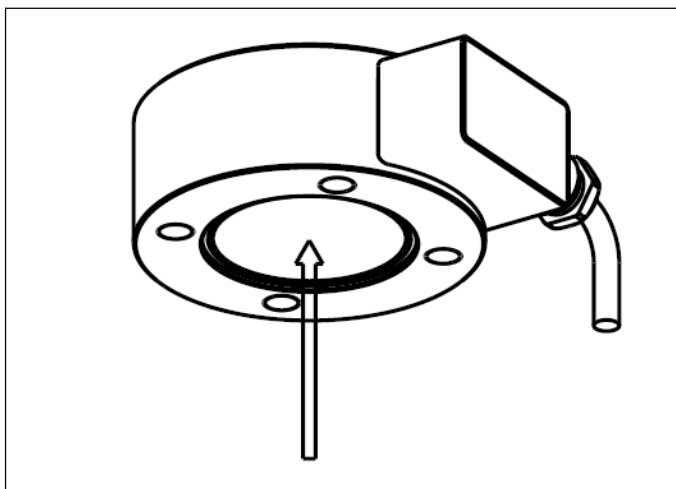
La lamina di protezione sul fondello del sensore non deve essere danneggiata, altrimenti si perde l'effetto dell'incapsulamento ermetico.
